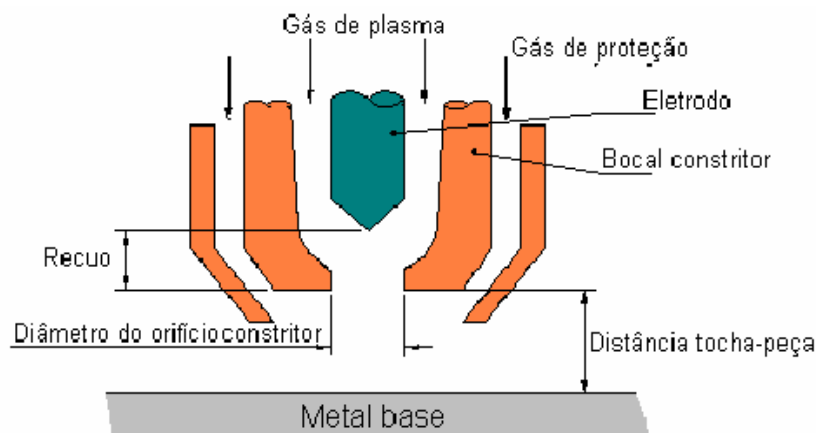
Identificação do Recuo do eletrodo e a configuração do bocal de soldagem Plasma.
